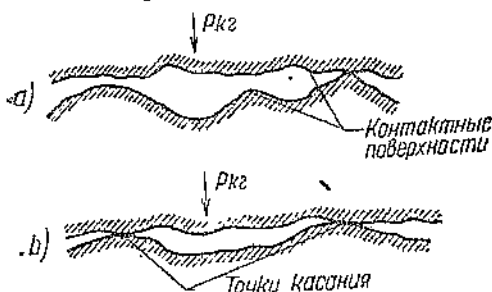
Обозначение контактных сопротивлений при точечной сварке нескольких листов.
